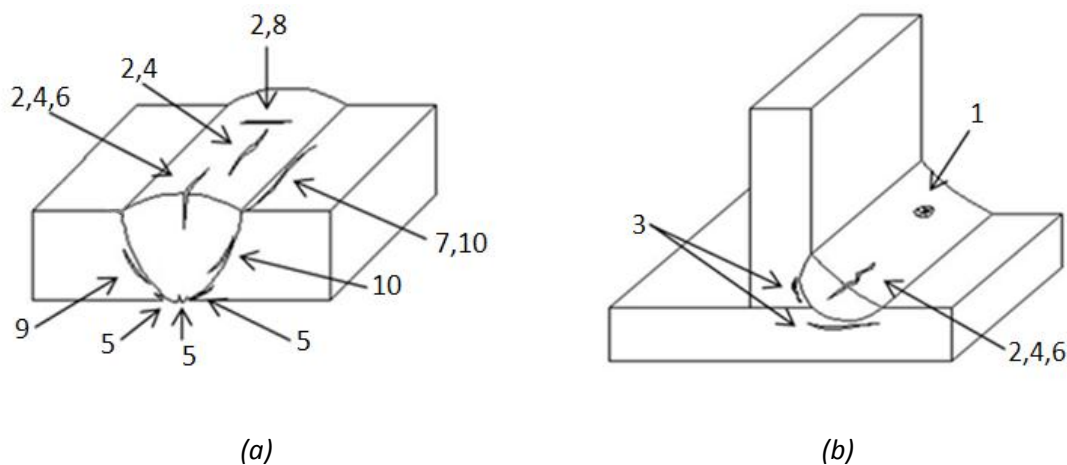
Tipos de fissuras em ligações soldadas: (a) soldadura de topo; (b) soldadura de ângulo.
